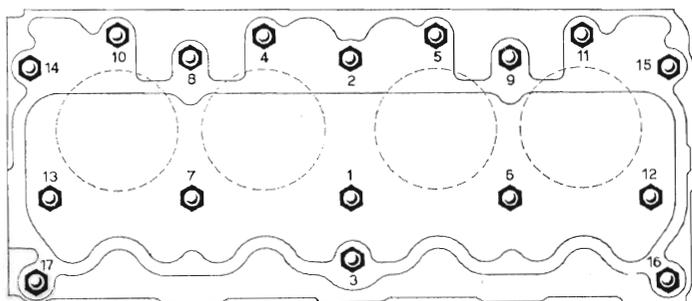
Ordine di chiusura dadi di fissaggio testa cilindri.
